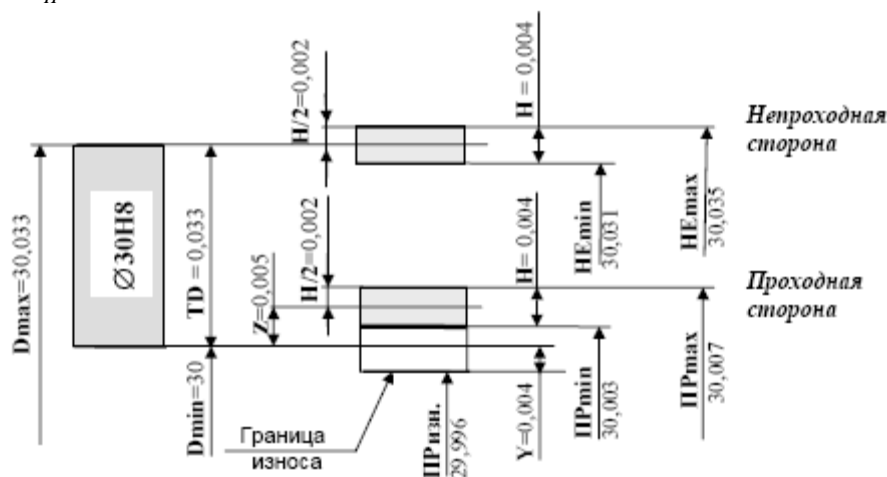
Схема расположения полей допусков отверстия ПР и НЕ сторон калибра-пробки
